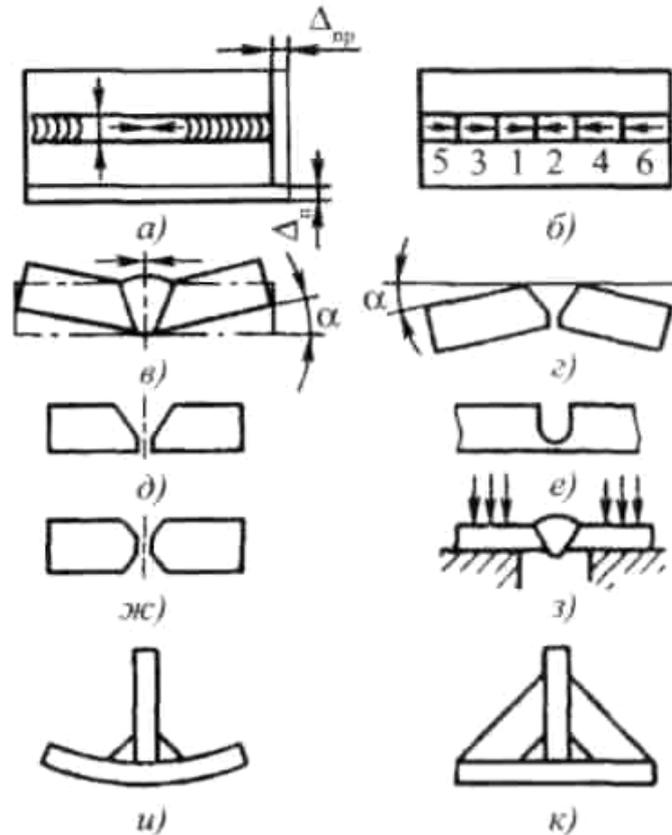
Усадка и угловая деформация сварных заготовок и способы их устранения:
